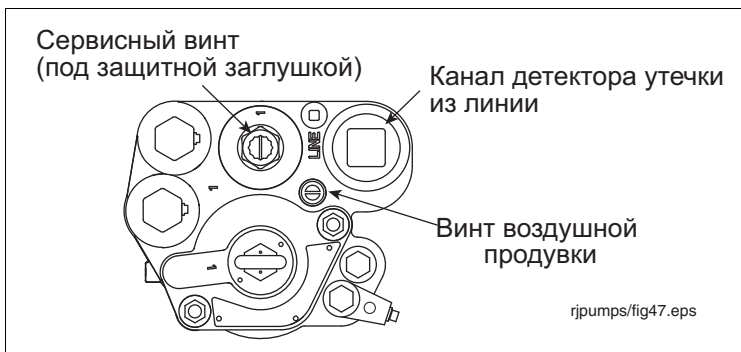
Расположение заглушки выпускного канала для датчика утечки из линии
